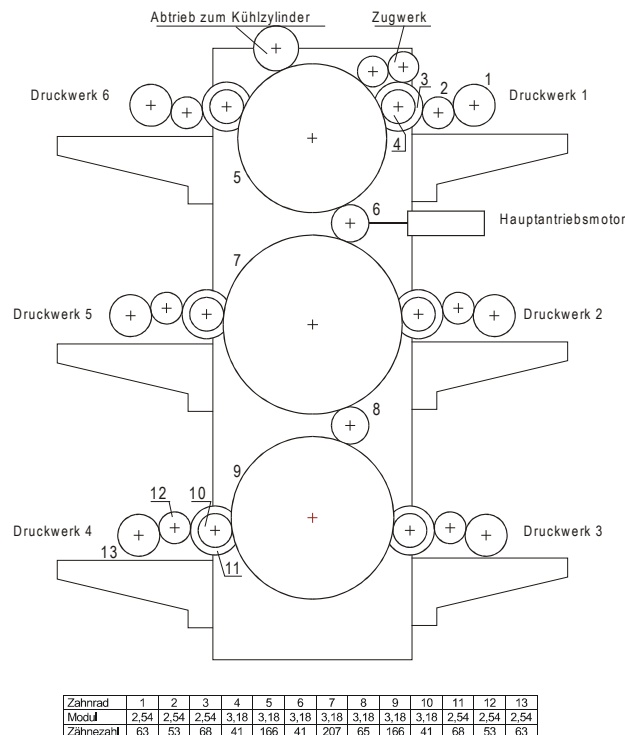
Zahnrad-Antriebsebene einer begutachteten Flexodruckmaschine
